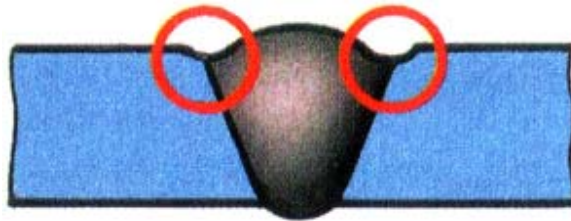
Дефект зварного з'єднання підріз
